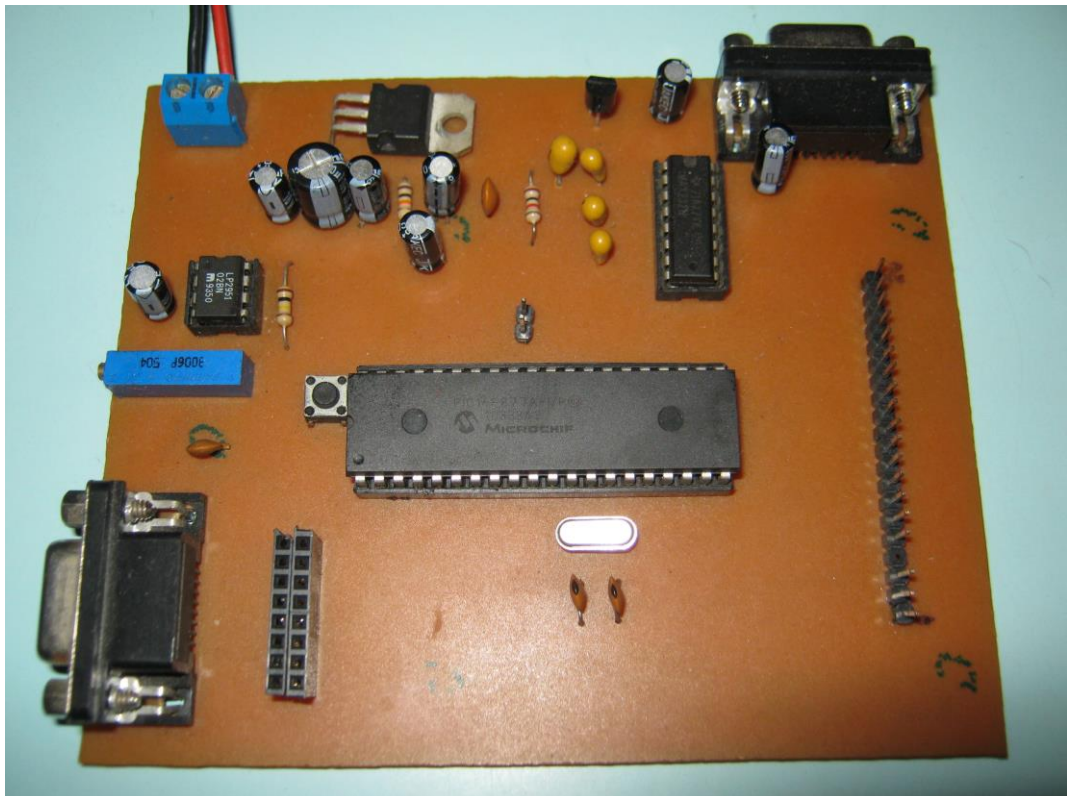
Tarjeta de Circuito Impreso (PCB) implementado.
